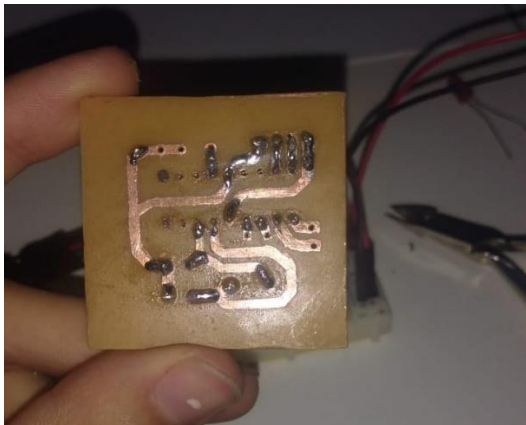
Placa Soldada. Desenvolvido pelos Autores.
